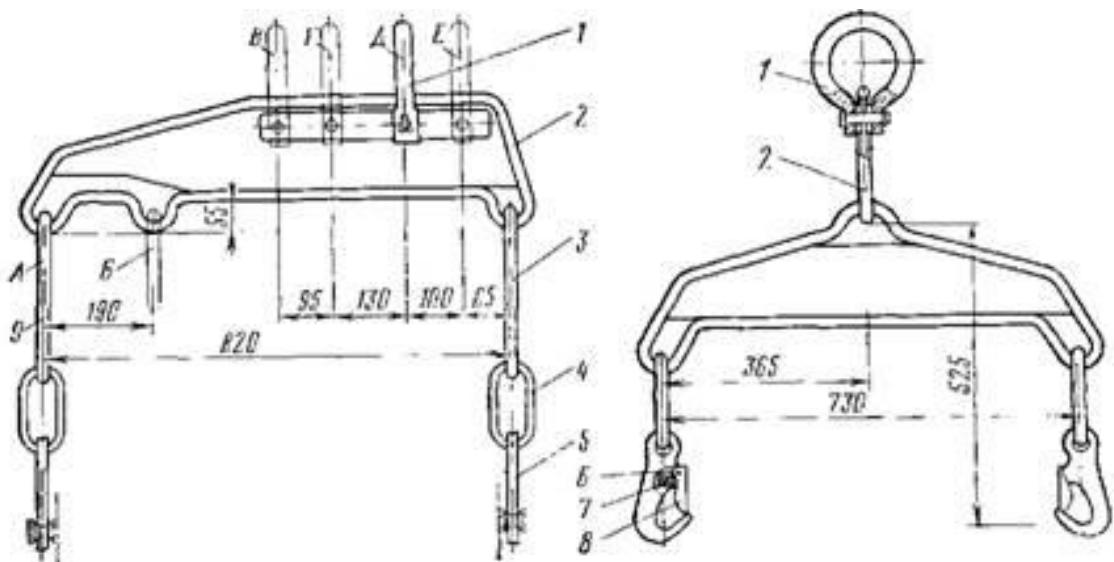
Универсальное приспособление для транспортировки двигателей
